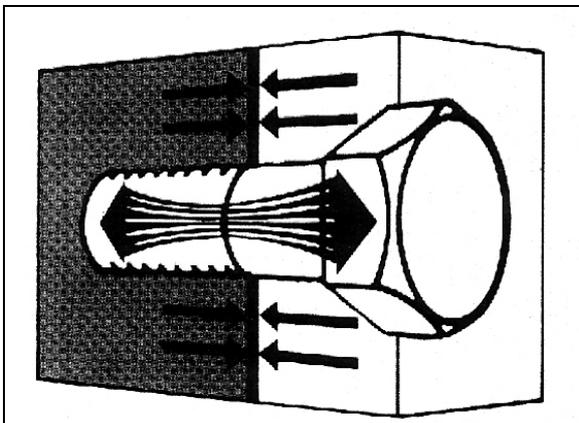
Equilibrio de fuerza en una unión atornillada ya ensamblada.
